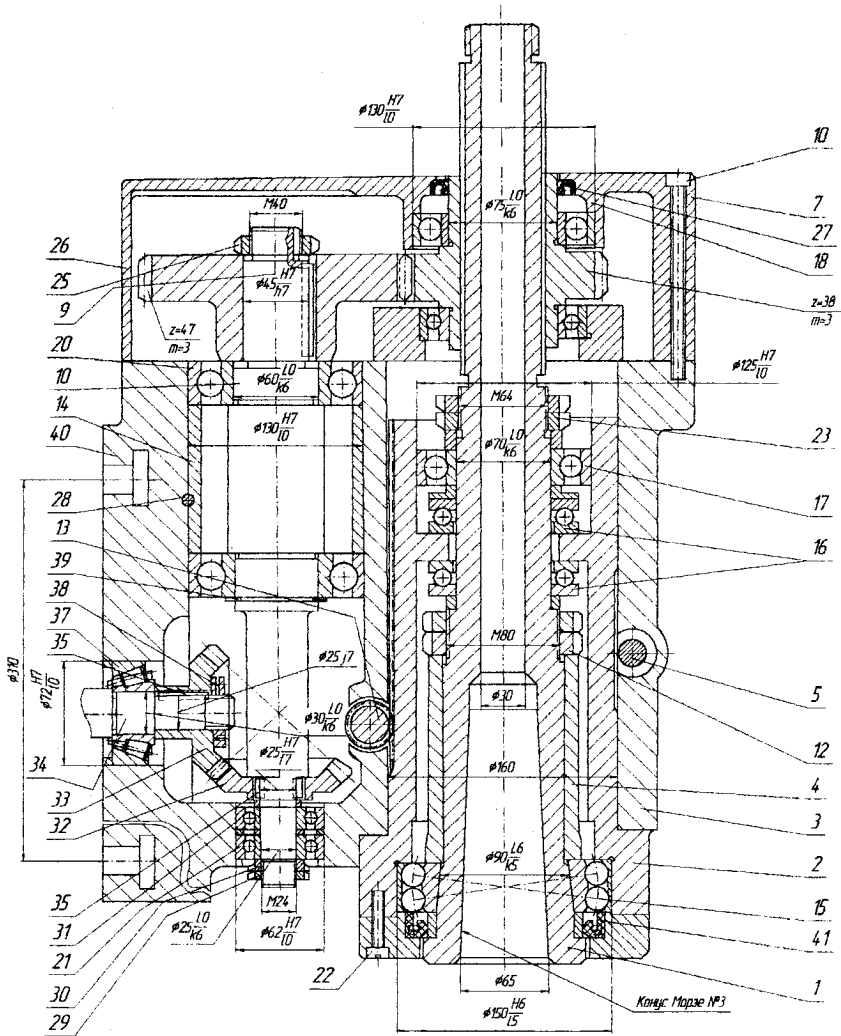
Поворотна шпиндельна головка вертикально-фрезерного верстага
